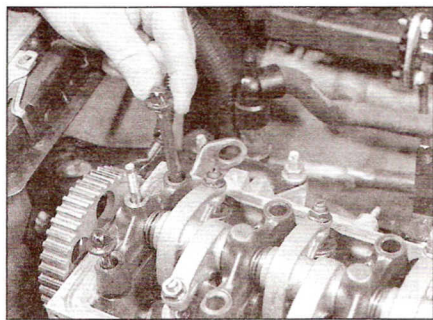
Отпустите и выверните болты крепления головки цилиндров (двигатели 1.4 л)
